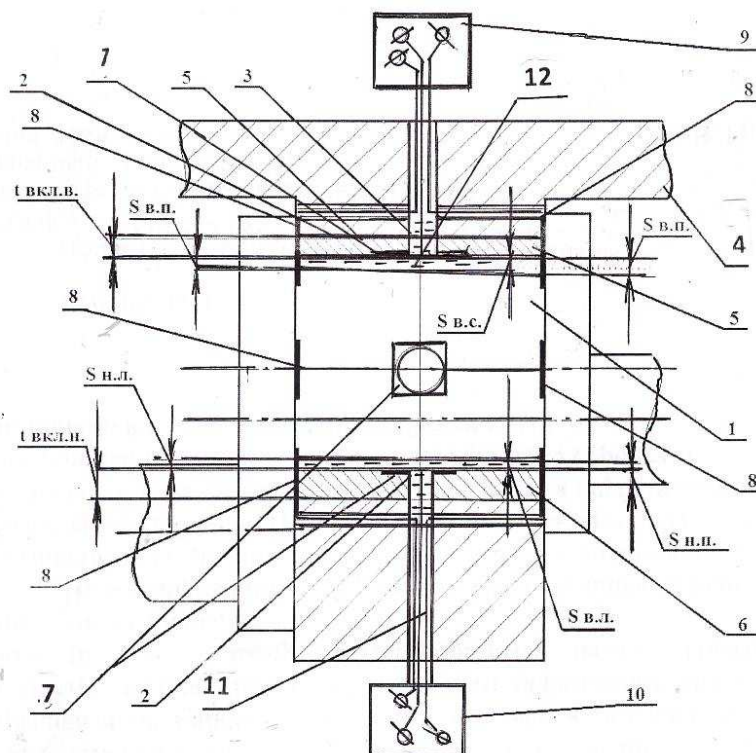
Продольное сечение охватываемой и охватывающей поверхностей подшипникового узла: 1-Охватываемая поверхность (вал), 2- подшипник скольжения; 3- сквозные каналы в охватывающей поверхности (подшипнике) 2; 4- картер; 5 – верхний вкладыш; 6— нижний вкладыш; 7 - датчики центральные для измерения истечения смазочного мала 5 через радиальные зазоры верхний левый, S в. п, нижний левый, S н. л., верхний средний Sv.с., нижний средний S н. с.. верхний правый Sv. п., нижний правый S н. п. подшипника; 8 – датчики в виде заглушек, предназначенные для измерения истечения смазочного мала через торцевые зазоры в подшипниках, установленные на торцах стенки картера 4 в районе вытекания смазочного масла после прохождения радиальных зазоров между рабочими цилиндрическими поверхностями 1 и 2 для слива в картер 4 через торцевые зазоры смазочной среды (масла) позицией не обозначено); 9- электропроводка, 10, - плато для электропроводки к приборам – осциллографу или ЭВМ; 11 – магистраль системы смазки; 12- смазочная среда (масло). Например: S в. п, T < S н. л., Sv.с., = S н. с.. Sv. п. T больше S н. п, или $S_{\min F} < S_T < S_{\text{опт}} < S_{\min F}$.
